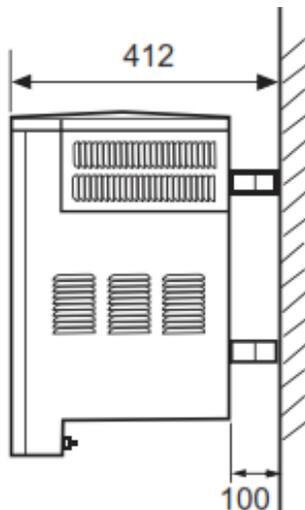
Dimensiones totales junto con los soportes de montaje en pared.
